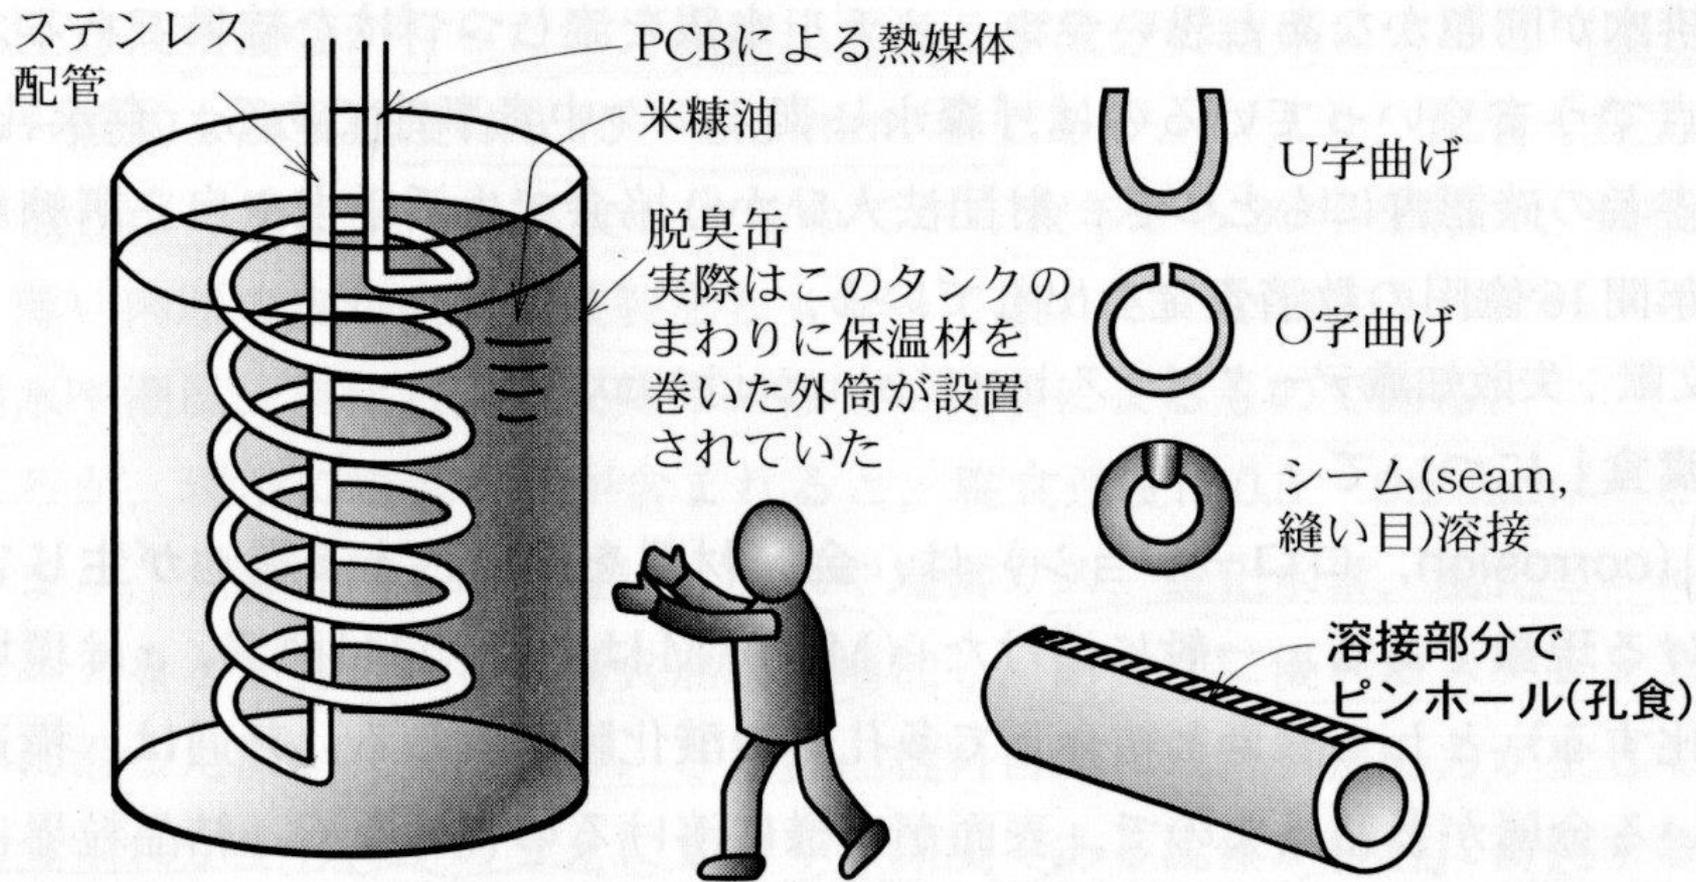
脱臭缶加熱コイルから PCB が米糠油に漏出
